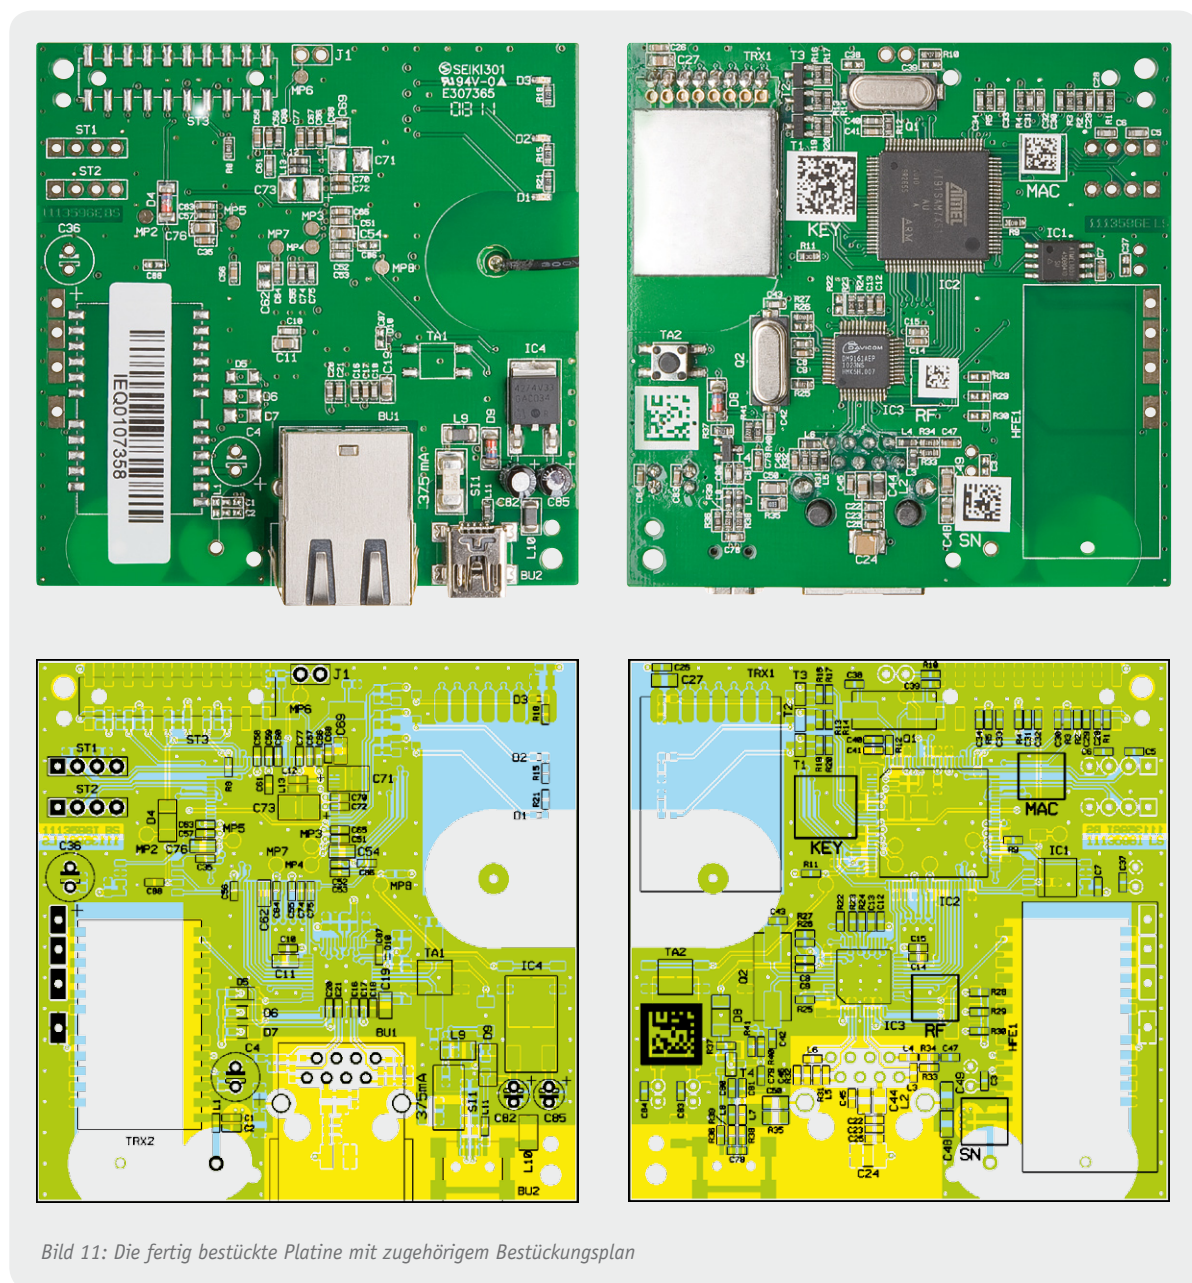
Die fertig bestückte Platine mit zugehörigem Bestückungsplan
